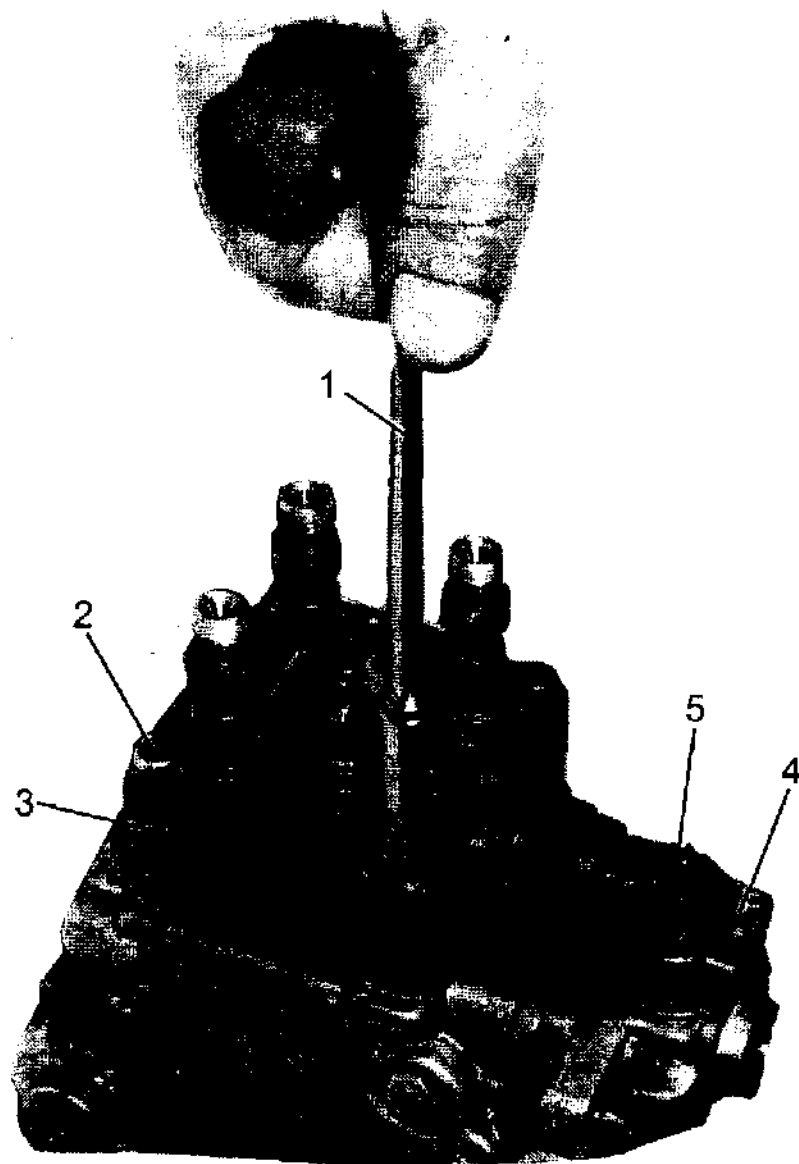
Извлечение головки ТНВД типа VE4 фирм "R. Bosch", "Nippon Denso", "Diesel-Kiki" из корпуса:
